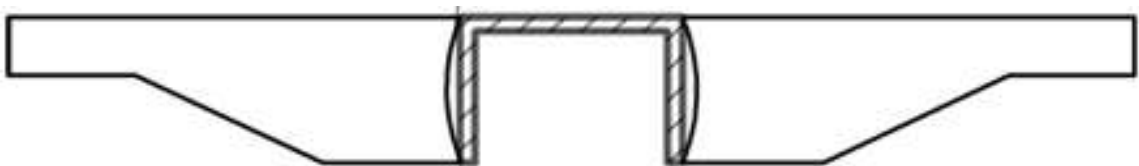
Концепт шарнірного зедання балок рами вагона-хопера для перевезення зерна
